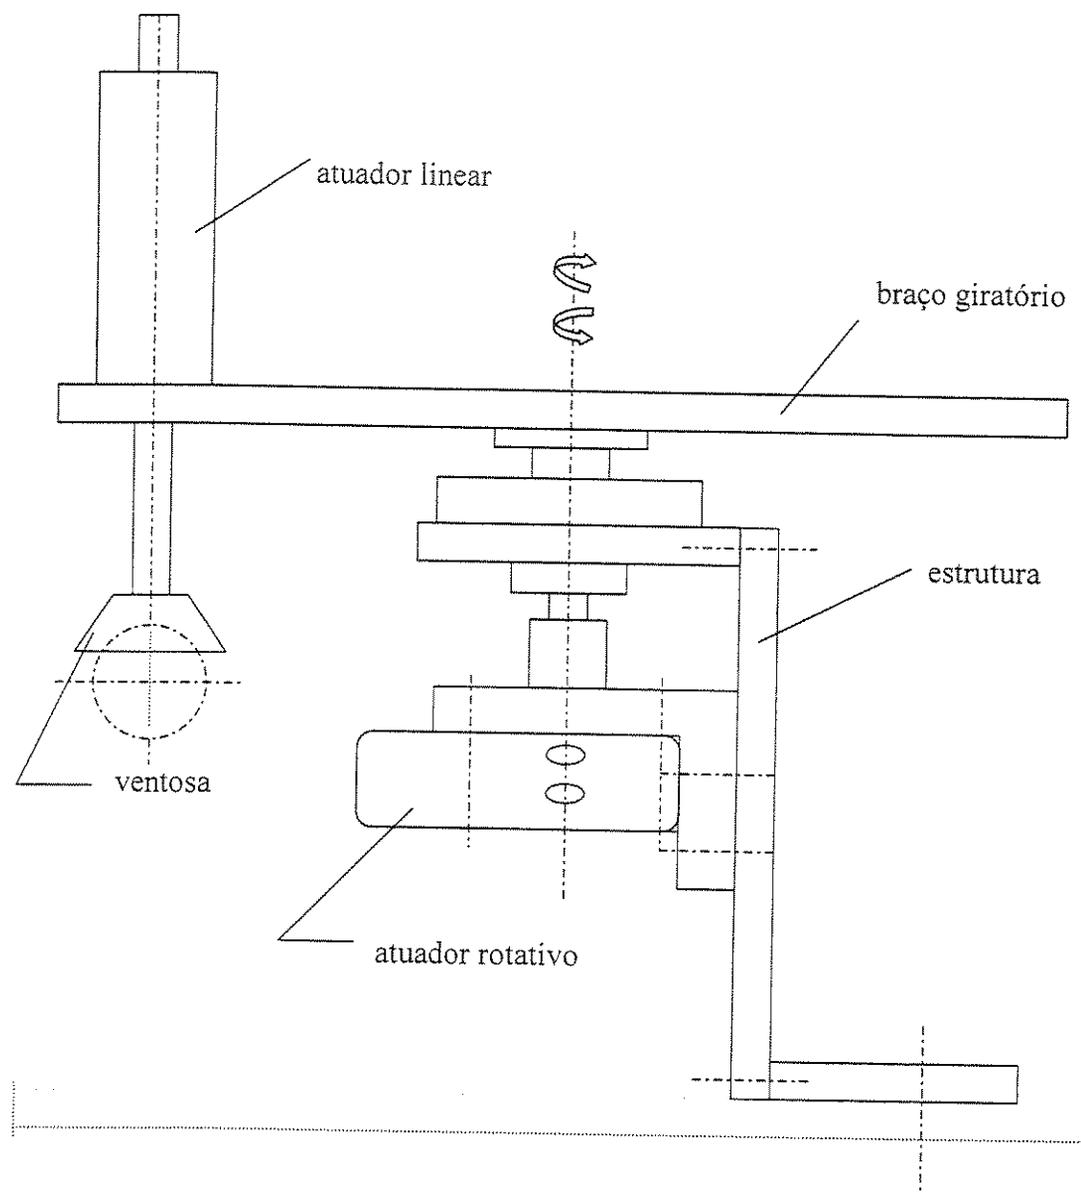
Esquema de Montagem do Manipulador Pneumático
